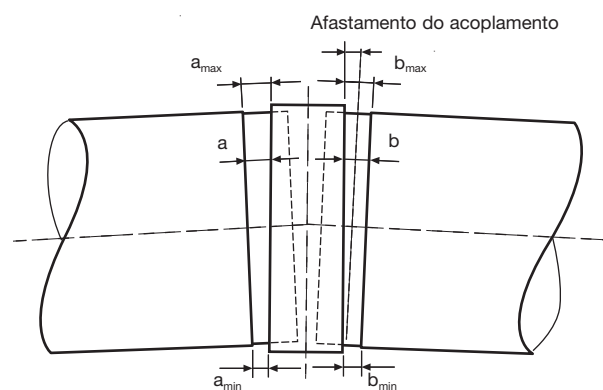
Medição da posição e desvio angular de um acoplamento
